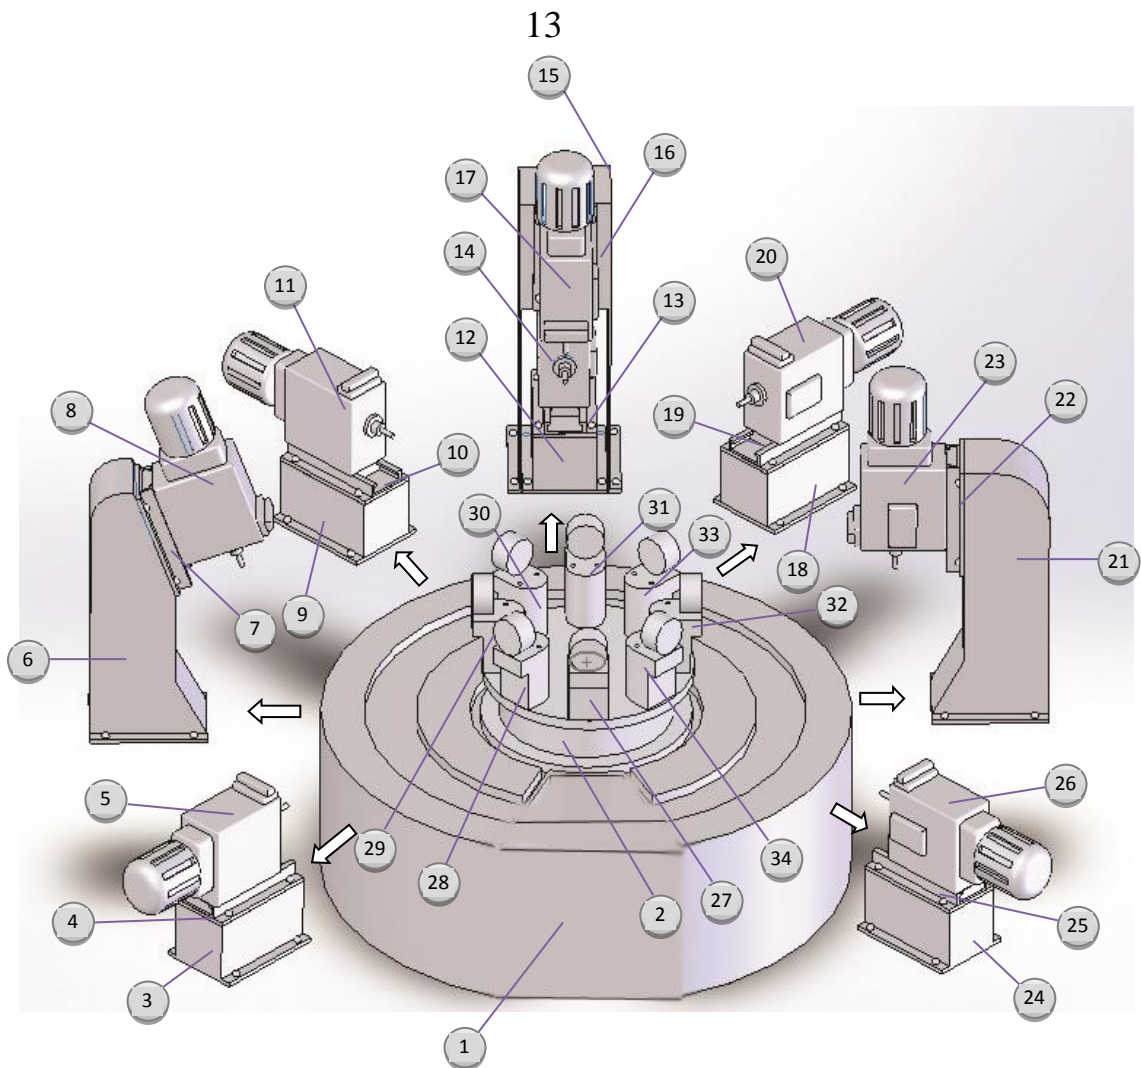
Разкомпоновка агрегатного верстата, підлягаючого реінжинірингу
